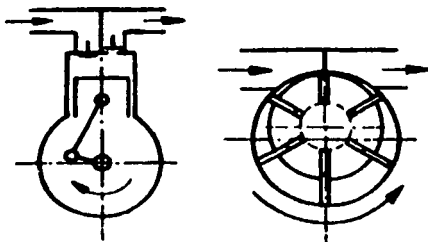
Disposición de un compresor de émbolo de una etapa y disposición de un compresor rotativo de paletas.
